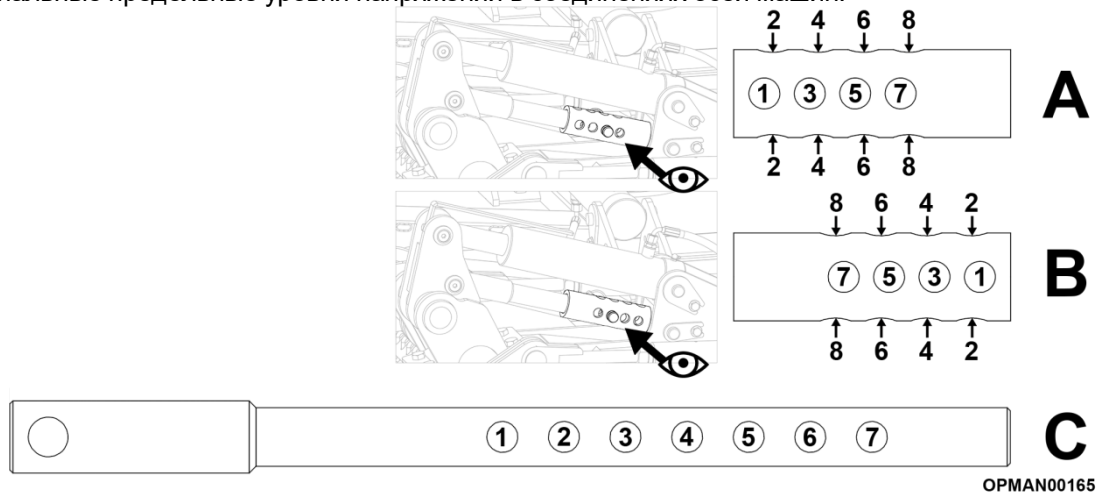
Multicut 460/620 Установка высоты резания
